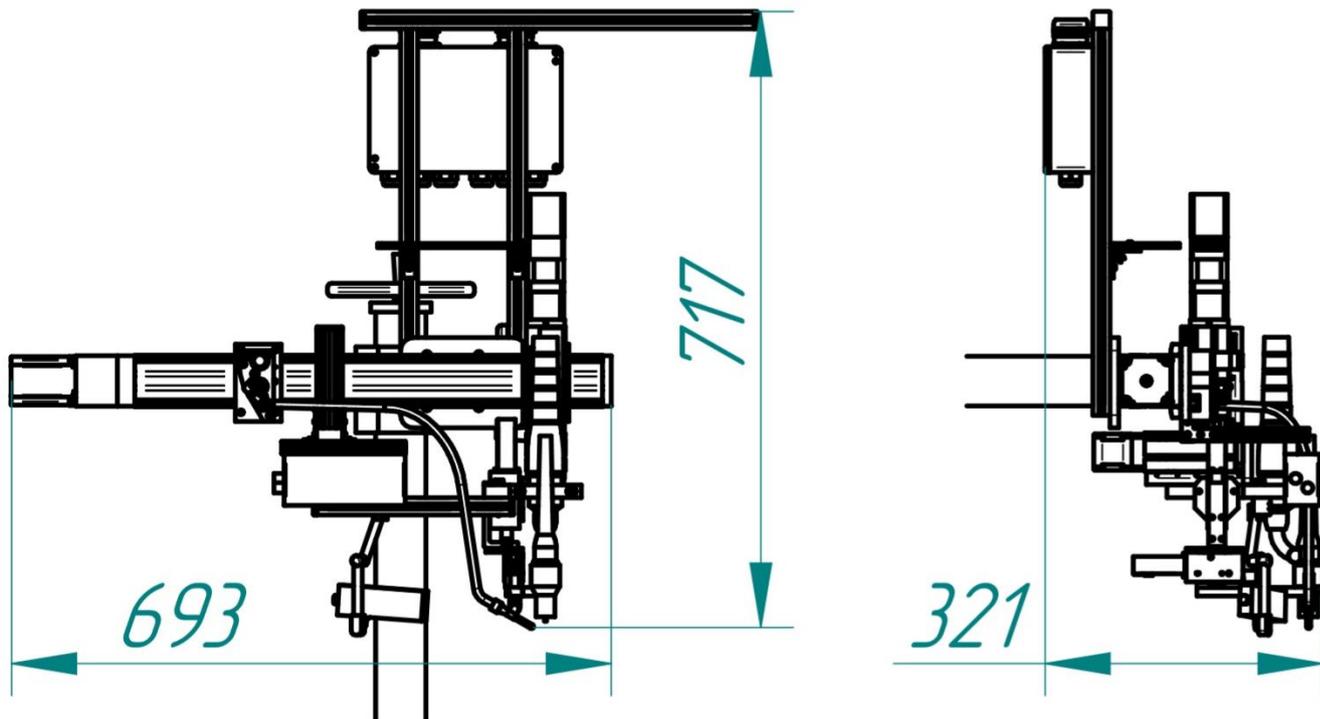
Габаритные размеры сварочной головки
